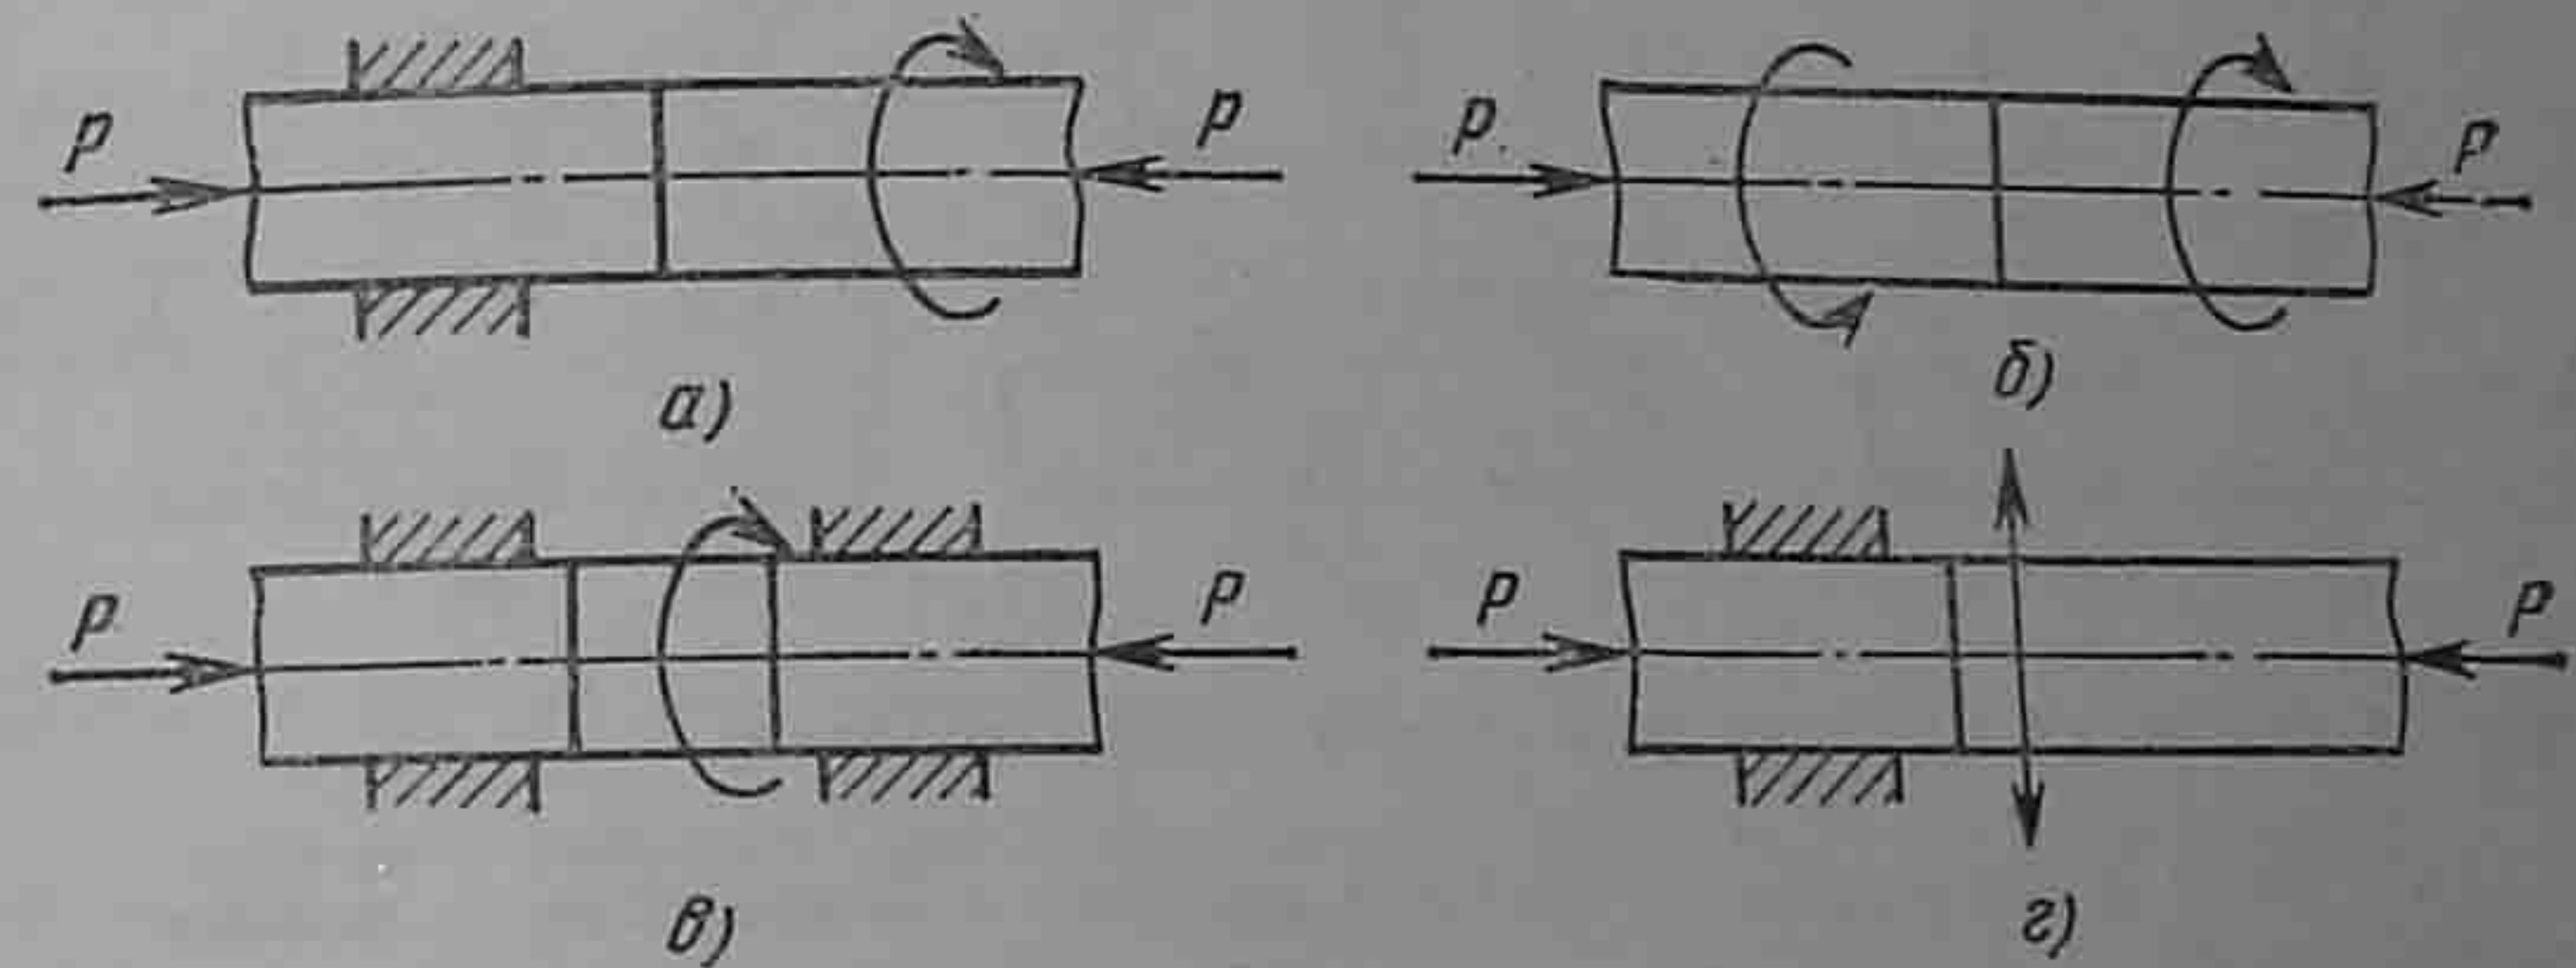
Принципиальные схемы сварки трением:
